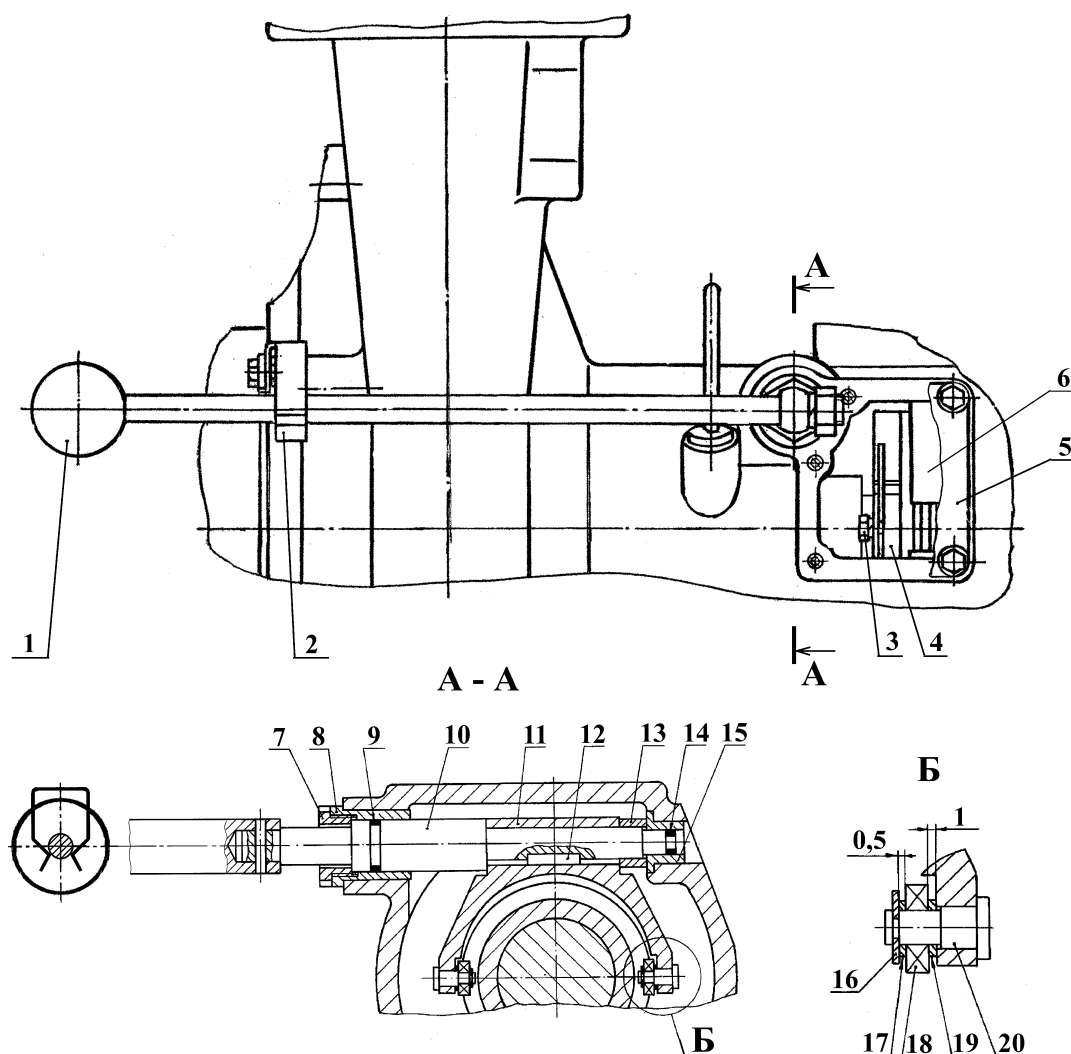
Механизм включения ступени высокого давления: 1 – рукоятка включения; 2 – пружинный фиксатор; 3 – стопорный болт; 4 – гайка регулировочная; 5 – крышка; 6 – ведомая шестерня; 7 – втулка ограничительная; 8 – втулка опорная; 10 – вал; 11 – вилка; 12 – шпонка; 13 – втулка ограничительная; 15 – втулка опорная; 16 – шайба стопорная; 17, 19 – шайба; 18 – подшипник; 20 – ось; 9, 14 – кольца уплотнительные.
